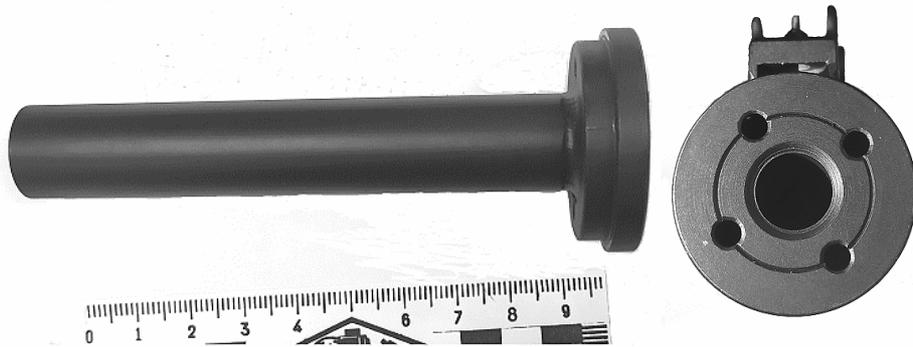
Съемная деталь корпуса имитатора глушителя СОК «МА-Винторез-7,62»
